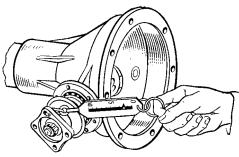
Проверка затяжки подшинииков вала ведущей шестерни
